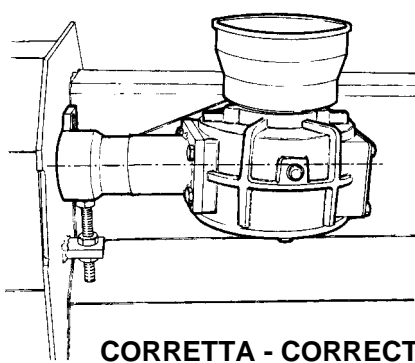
Posizione scatola ingranaggi - Gearbox position
